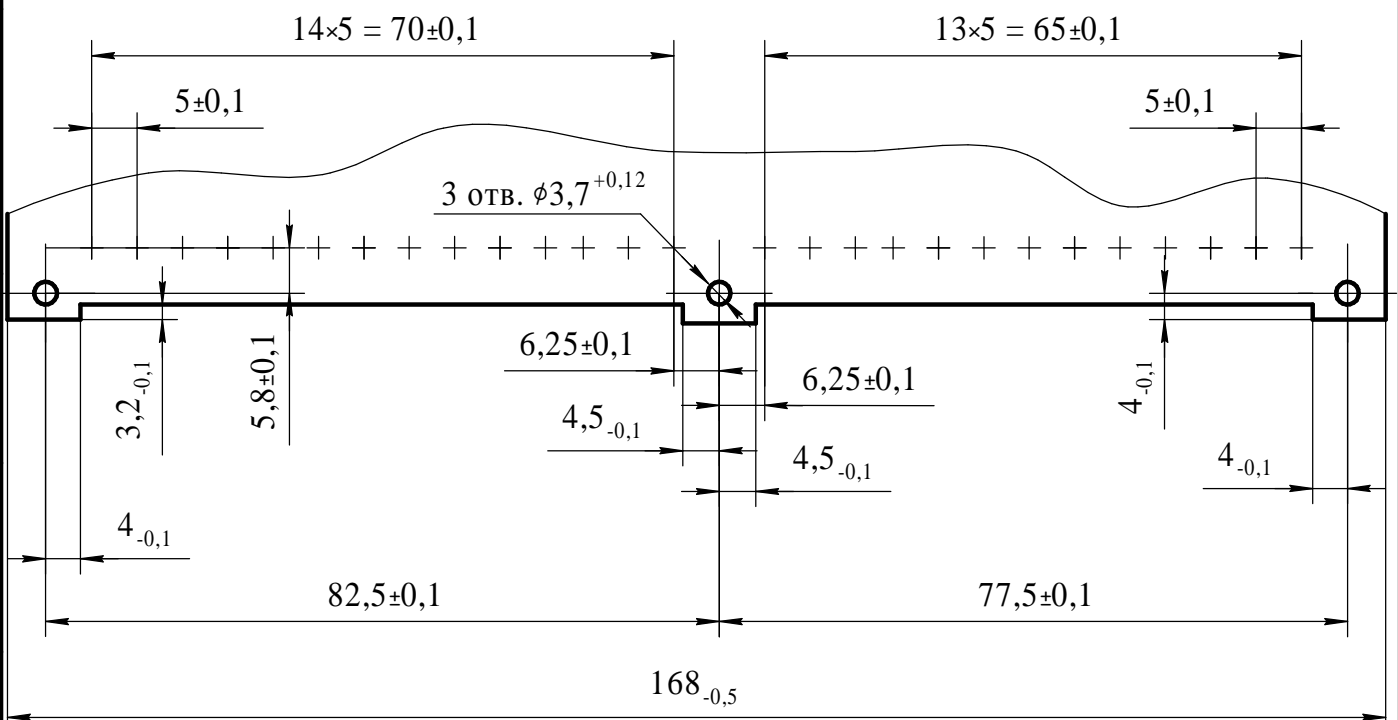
Вилка ГРППЗ-58ШЭ
